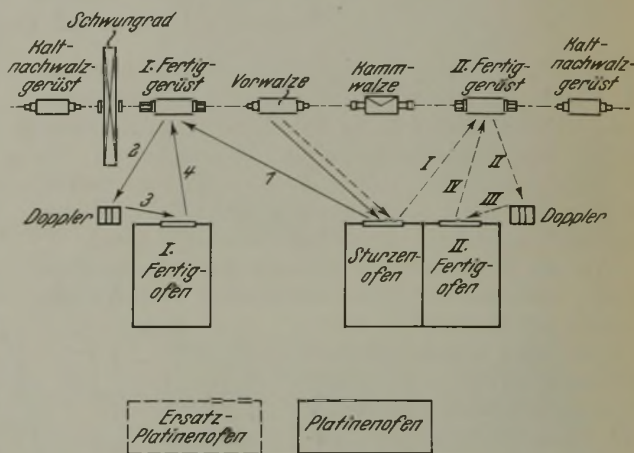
Grundriß der Feinblech-Walzwerksanlage.
